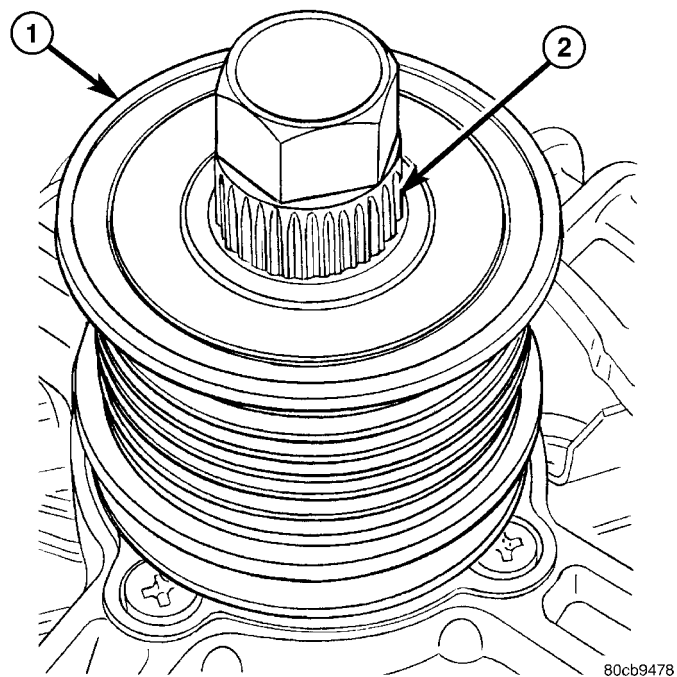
HERRAMIENTA N° 8823 (VM.1048) Y DESACOPLADOR INA
